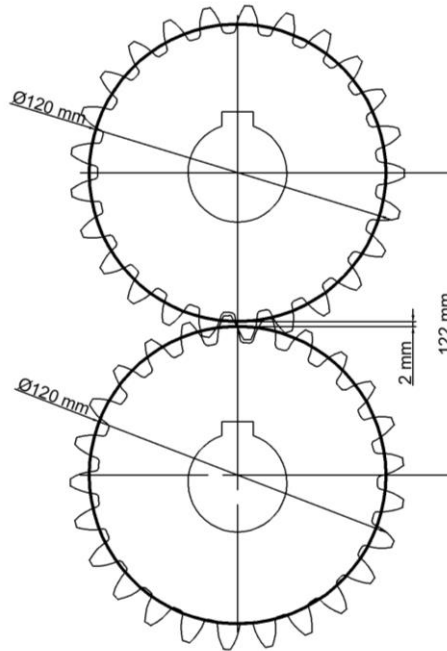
Posicionamiento de los rodillos y engranajes para determinar C
